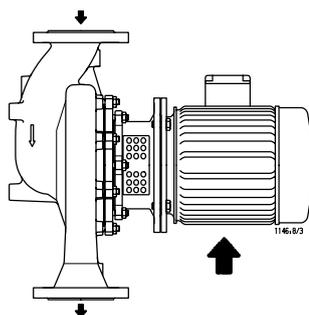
Montagem na horizontal, sentido do fluxo de cima para baixo
